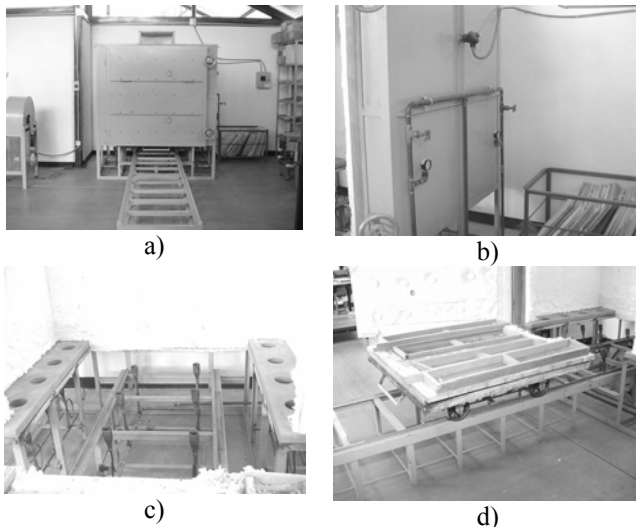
Horno del taller. (a) Vista frontal, (b) válvulas e indicadores, (c) quemadores y (d) carro.
